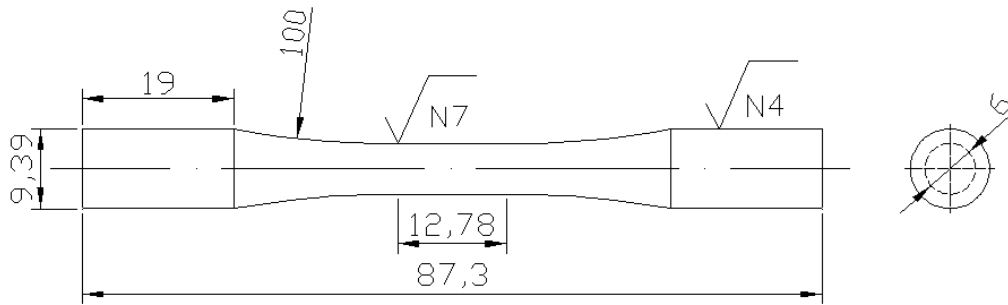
Probeta de fatiga rotativa. Dimensiones en mm.
